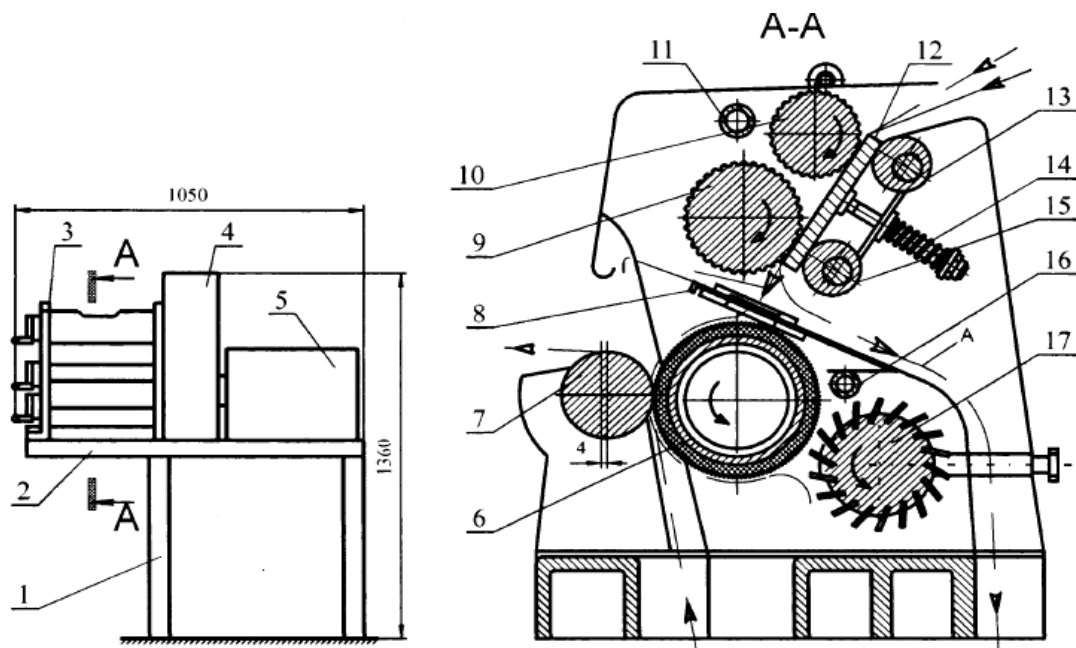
Універсальна машина ФОК для попереднього і кінцевого очищення кишок усіх видів забійних тварин: 1 – стійки; 2 – плита; 3 – бокові пластини; 4 – редуктор; 5 – електродвигун; 6 – очищувальний рифлений прогумований валик; 7 – ексцентриковий вал; 8 – щиток; 9 – подрібнювальний валик; 10 – подавальний валик; 11, 16 – форсунки; 12 – пластина; 13, 15 – ексцентрики; 14 – пружина; 17 – пластинчастий валик; А – свинячі й баранячі кишки; Б – яловичі та кінські кишки
